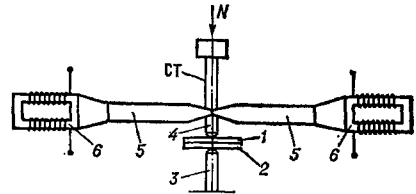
Схема установки для ультразвуковой сварки с изгибными колебаниями: 1—6 — то же, что и на рис. 1; преобразователи работают в противофазе; СТ — изгибно колеблющийся стержень.
